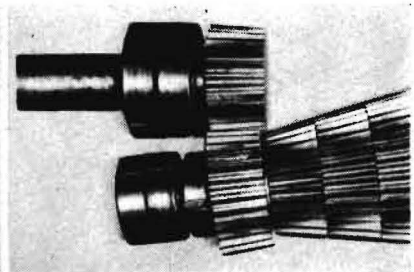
Zahnbrüche bei einer fliegenden Wel-lenlagerung
